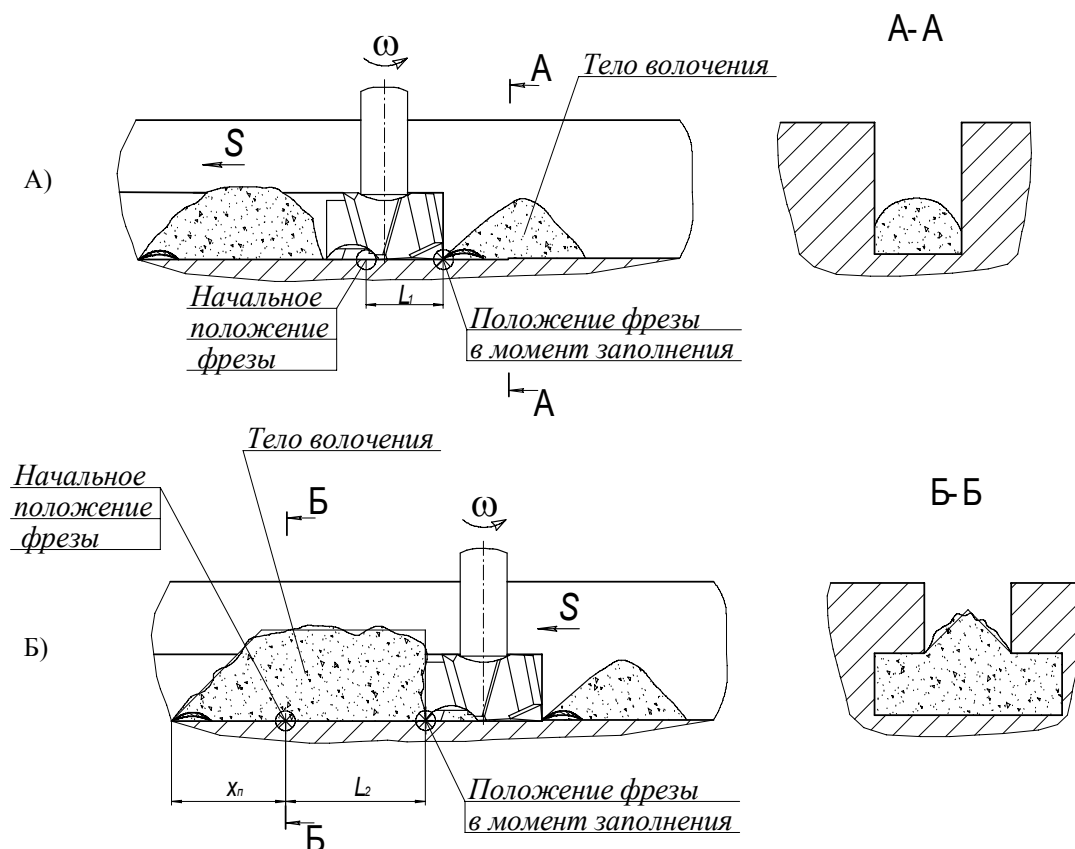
Схема заполнения стружкой пазов при их фрезеровании: а) прямоугольного паза; б) Т-образного паза
